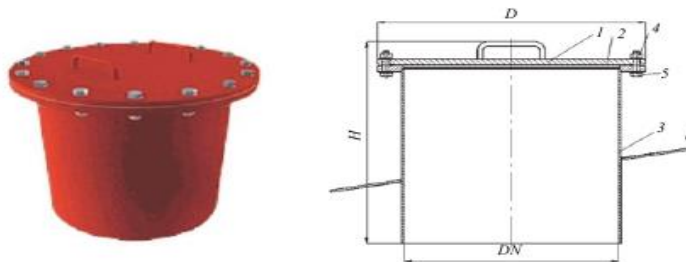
Люк світловий: 1 - кришка; 2 - прокладка; 3 - корпус; 4 - гайка; 5 - болт; 6 - підсилююча накладка
